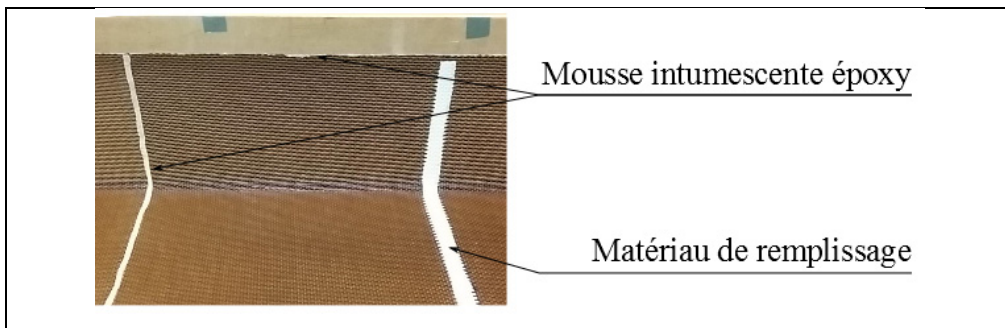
Disposition des matériaux d'assemblage et de renforcement local
